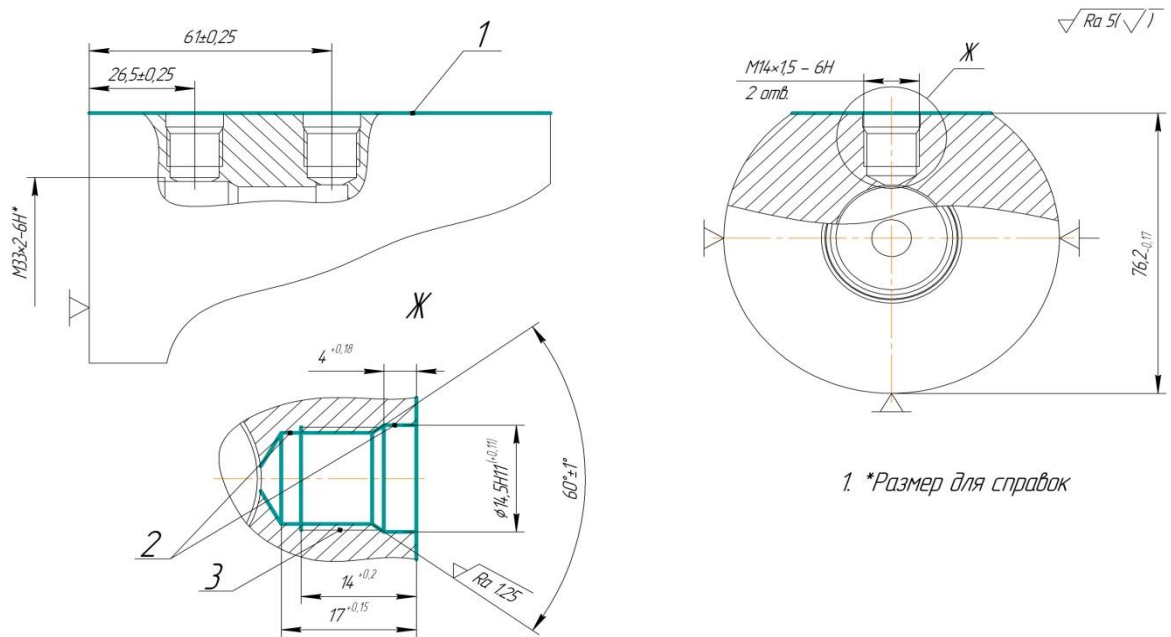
Операционный эскиз фрезерной обработки
